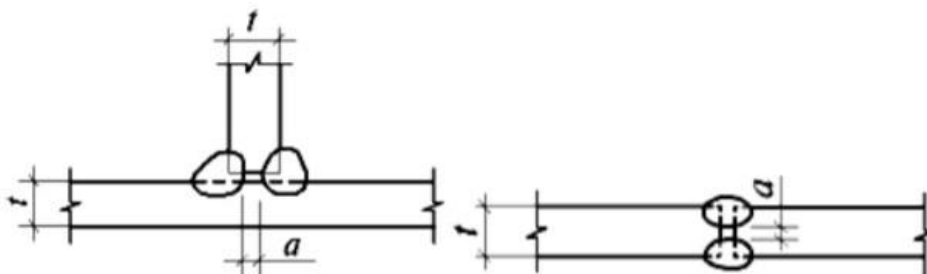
Непровар в корне шва при двусторонней сварке в угловых и стыковых соединениях
